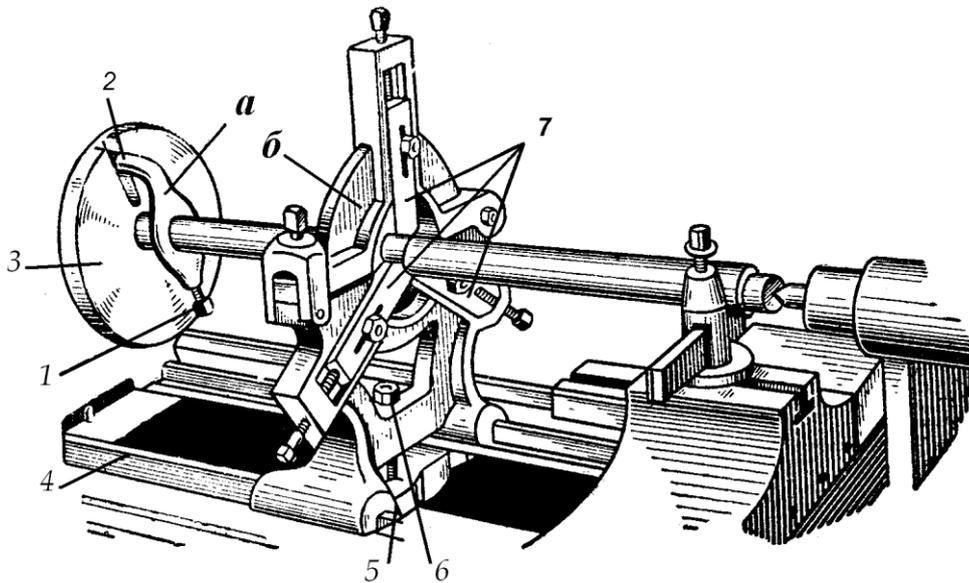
Точение в центрах с неподвижным люнетом: а – хомут; б – неподвижный люнет; 1 – винт; 2 – палец; 3 – планшайба; 4 – станина; 5 – планка; 6 – болт с гайкой; 7 – упоры
